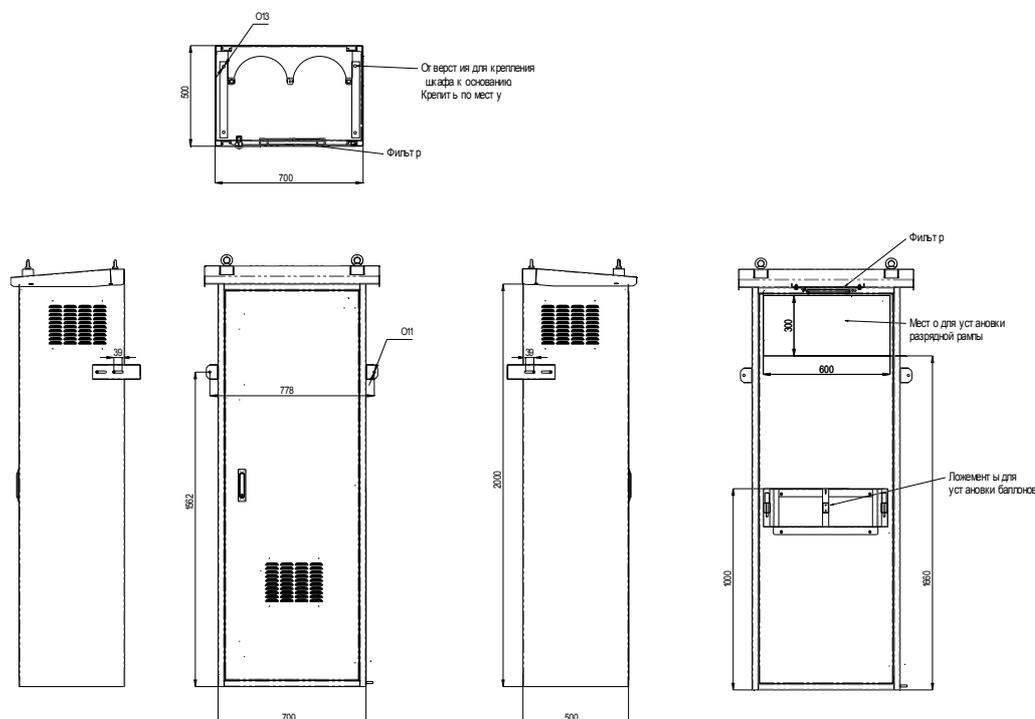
Габаритный чертеж шкафа 1875У1
